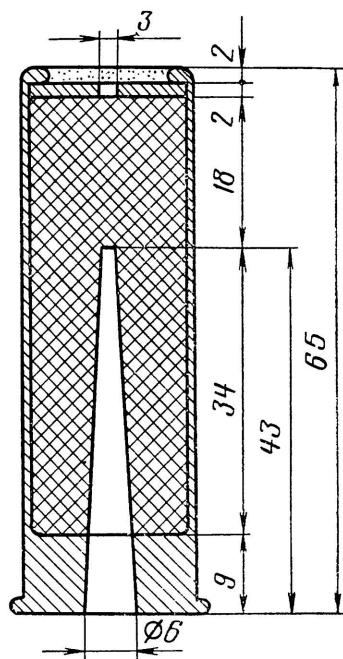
Корпус и двигатель ДБ-1-СМ-6
